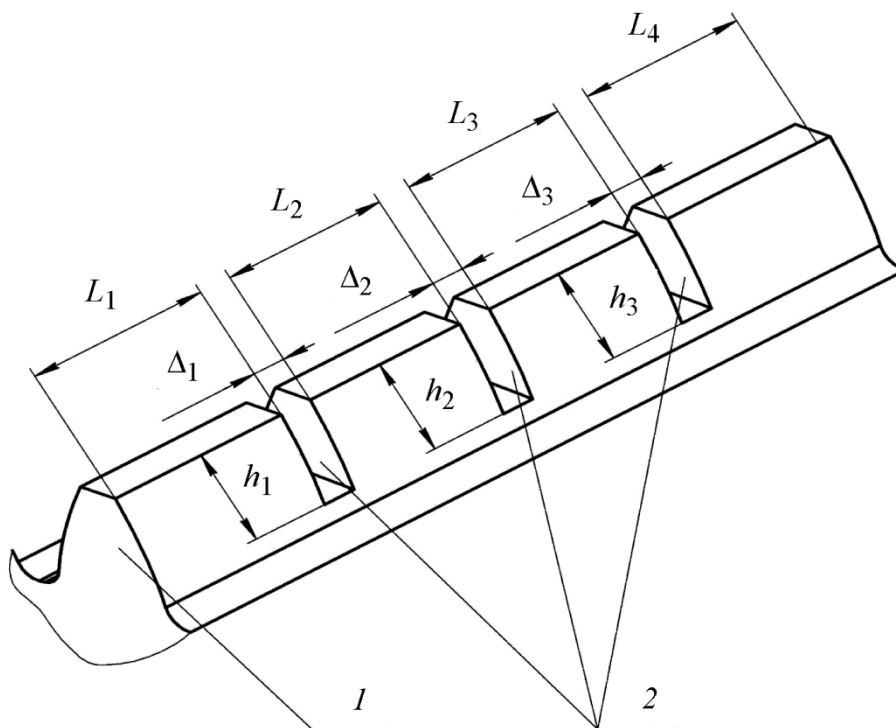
Зуб зубчатой обоймы с кольцевыми канавками: 1 – венец зубчатого колеса; 2 – кольцевые канавки; $L_1 = L_2 = L_3 = L_4$ – размеры участков; $h_1 = h_2 = h_3$ $h_4 = 1,5 m$ – глубина кольцевых канавок (здесь m – модуль зубчатого колеса); $\Delta_1 = \Delta_2 = \Delta_3 = 1$ мм – ширина кольцевых канавок
